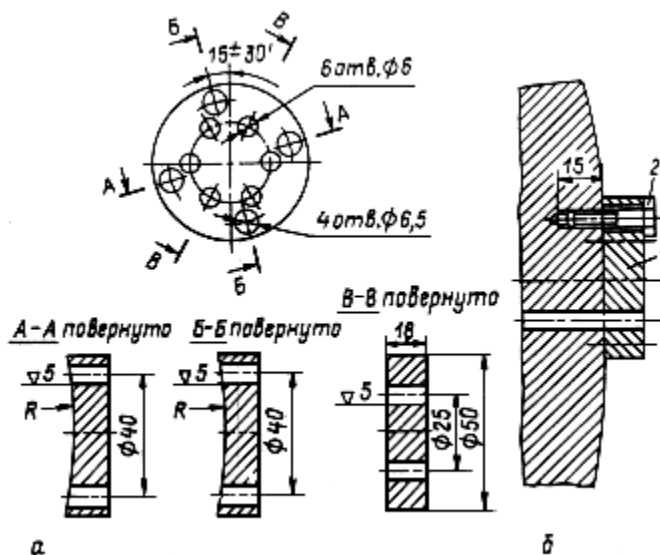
Кондуктор для вырезки образца из штуцера: а - устройство; б - установка штуцера; 1 - кондуктор; 2 - болт М6 × 25
